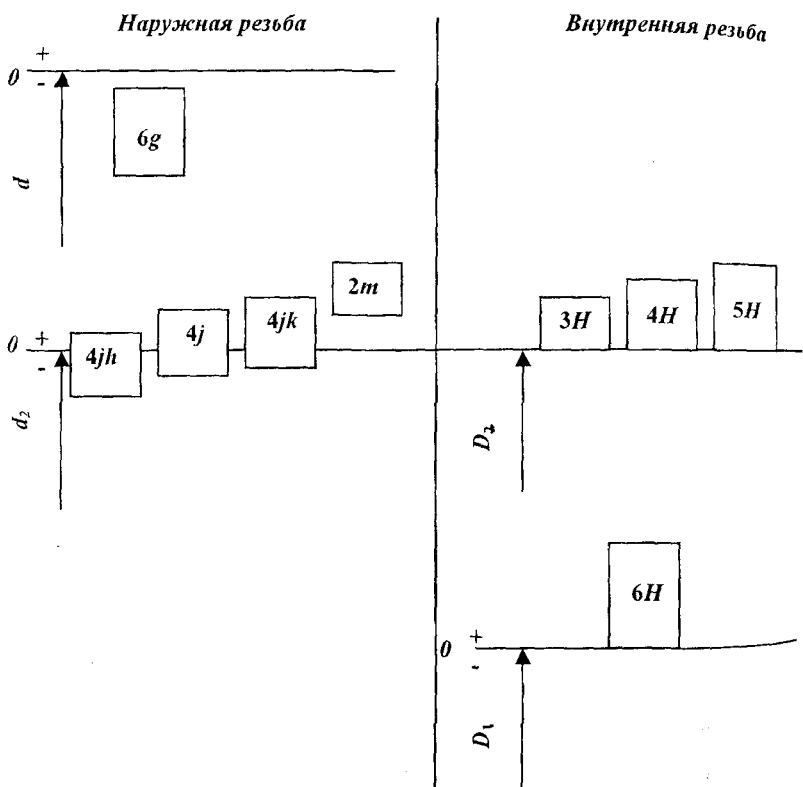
Поля допусков резьб для соединений с переходными посадками
